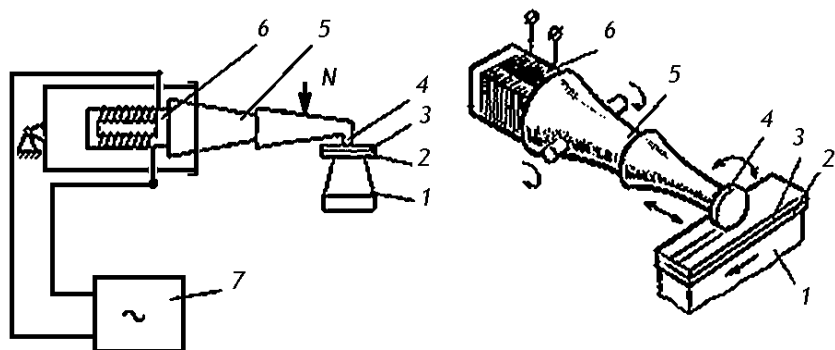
Ультразвуковая сварка, где 1 – опора; 2, 3 – свариваемые детали; 4 – сварочный инструмент; 5 – волновод; 6 – электроакустический преобразователь; 7 – ультразвуковой генератор; N – заданное усилие.
